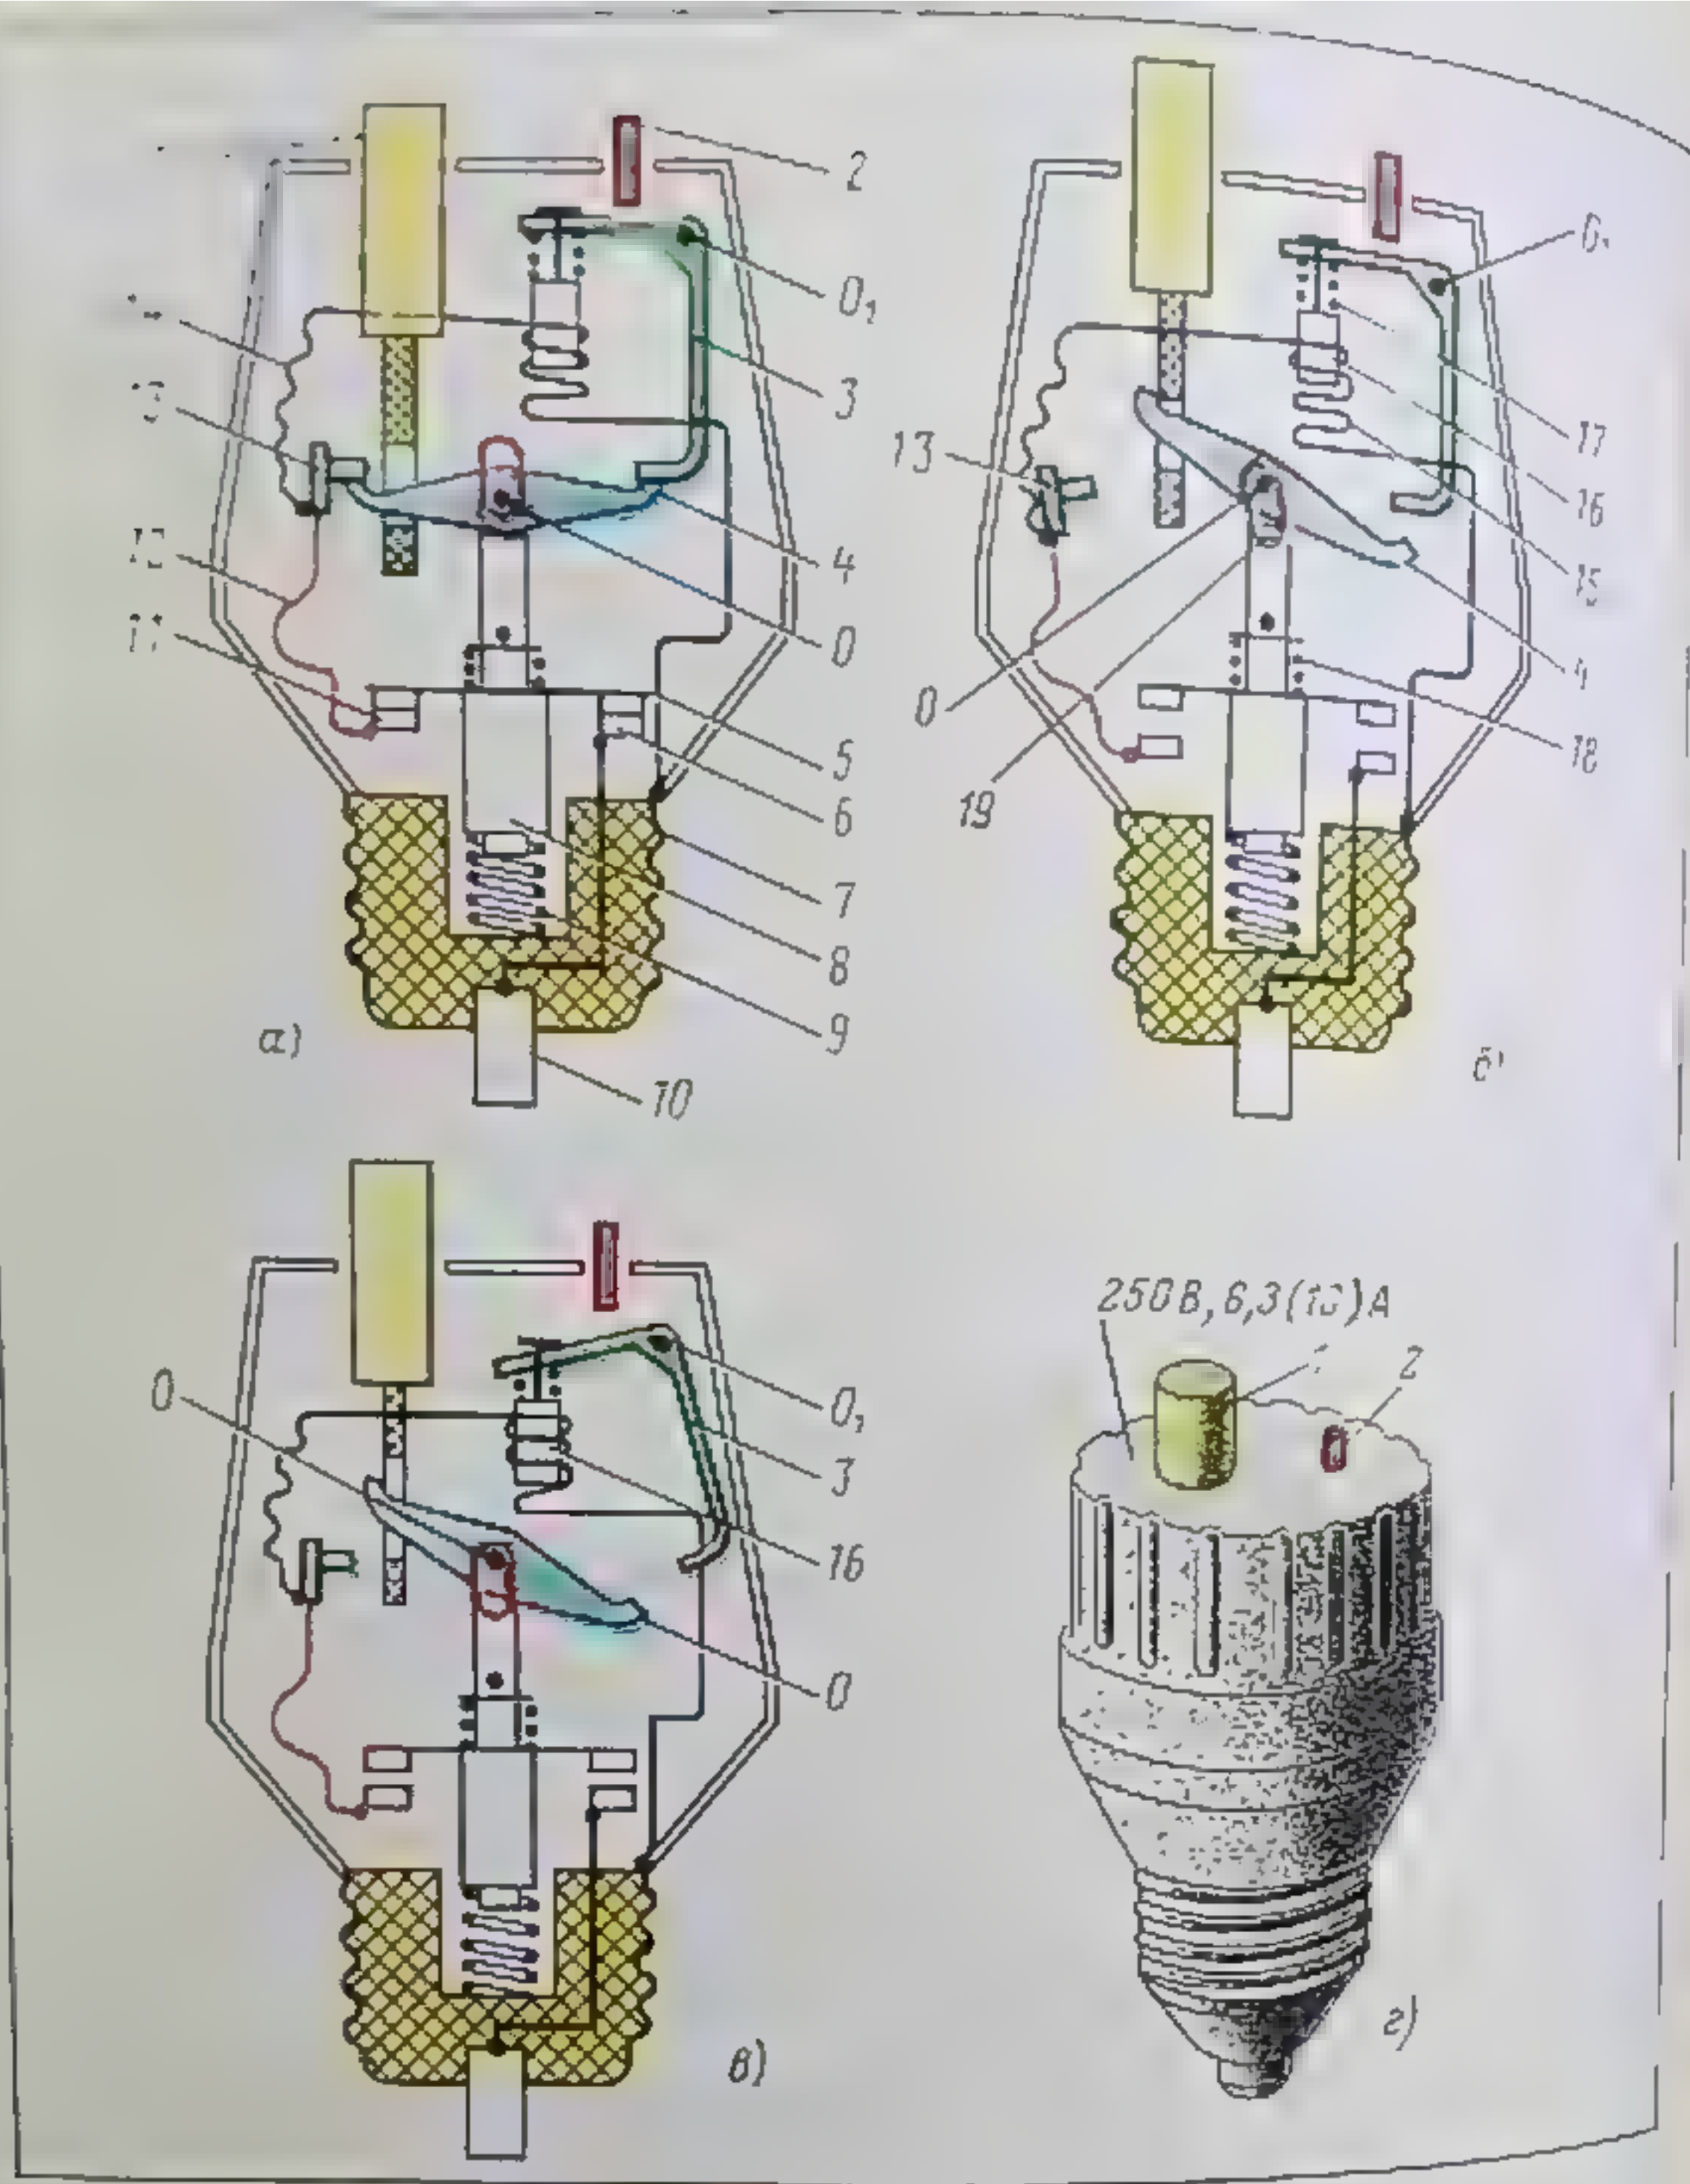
Предохранитель автоматический резьбовой (автоматический выключатель), ввертывающийся в корпус предохранителя взамен пробки;
